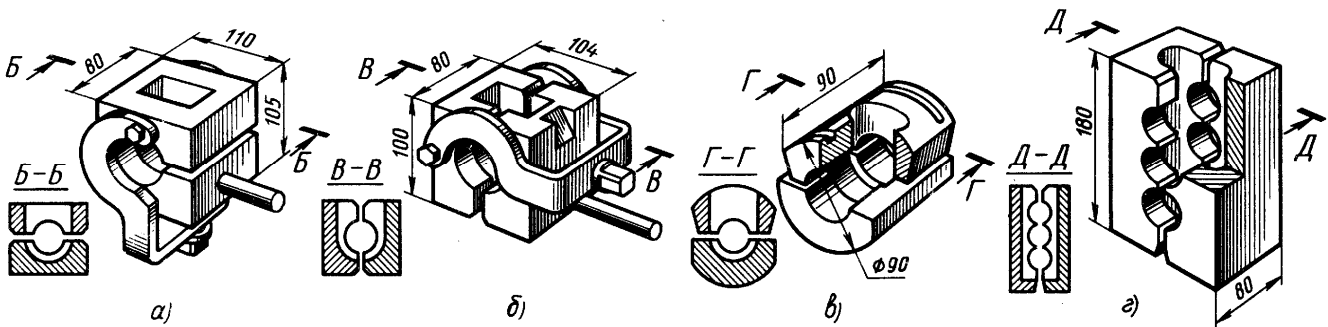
Инвентарные составные медные формы с канавками для сварки стыковых соединений горизонтальных стержней
